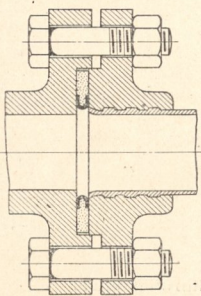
Asbestring mit innerer Kupfereinfassung.
